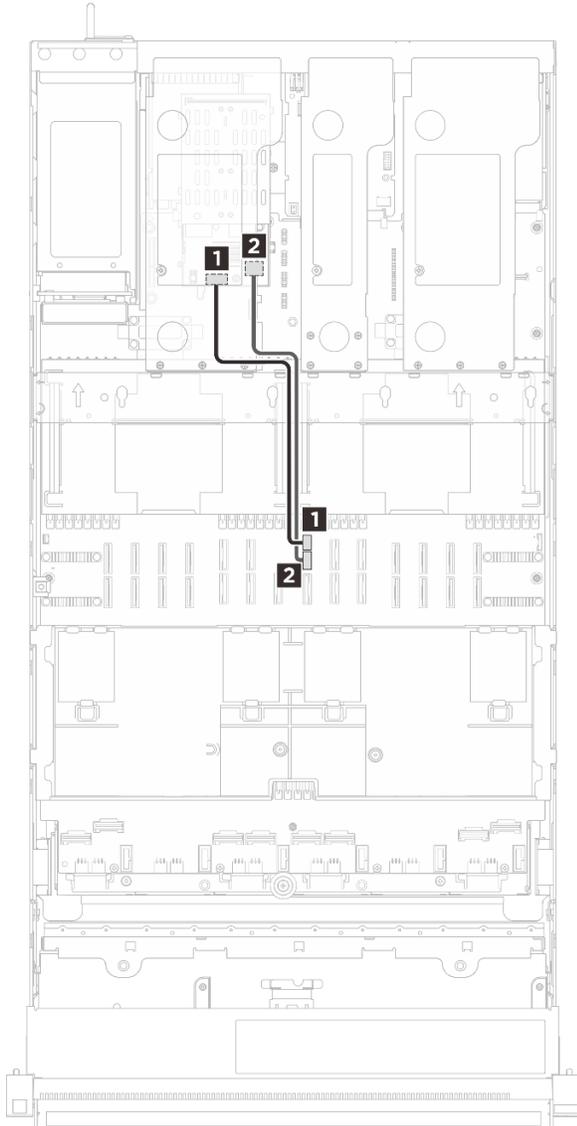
Cheminement des câbles pour le fond de panier arrière M.2
